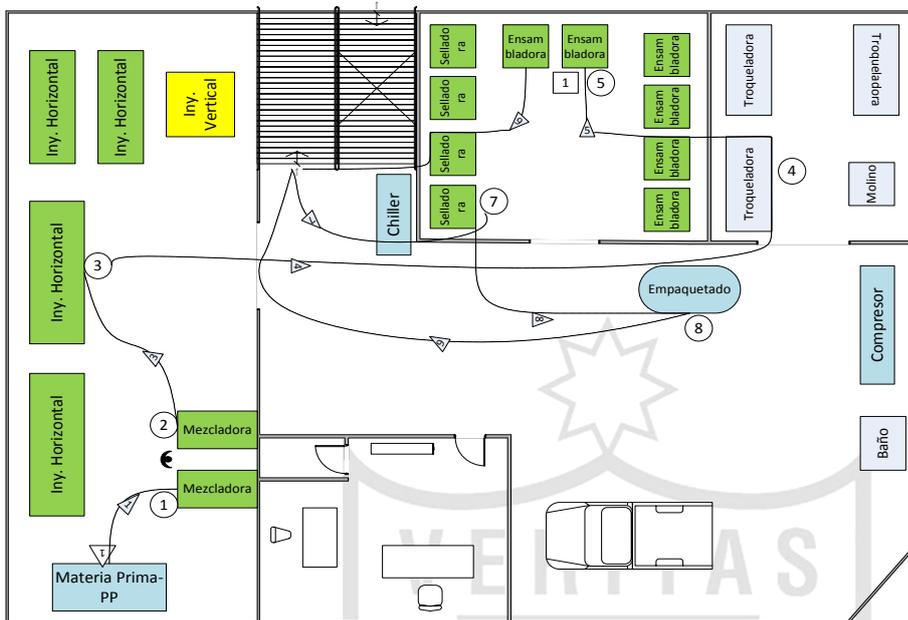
Plano: Vista de Planta del 1er piso de la empresa LEÓN PLAST con la nueva redistribución.
